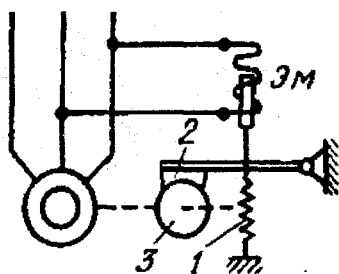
Схема электромагнитного тормоза: 1 – пружина, 2 – колодка тормозная, 3 – шкив тормозной
